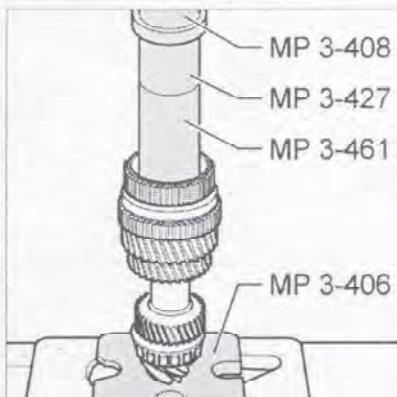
Напрессуйте ступицу синхронизатора 1-й/2-й передач на вал до упора.
